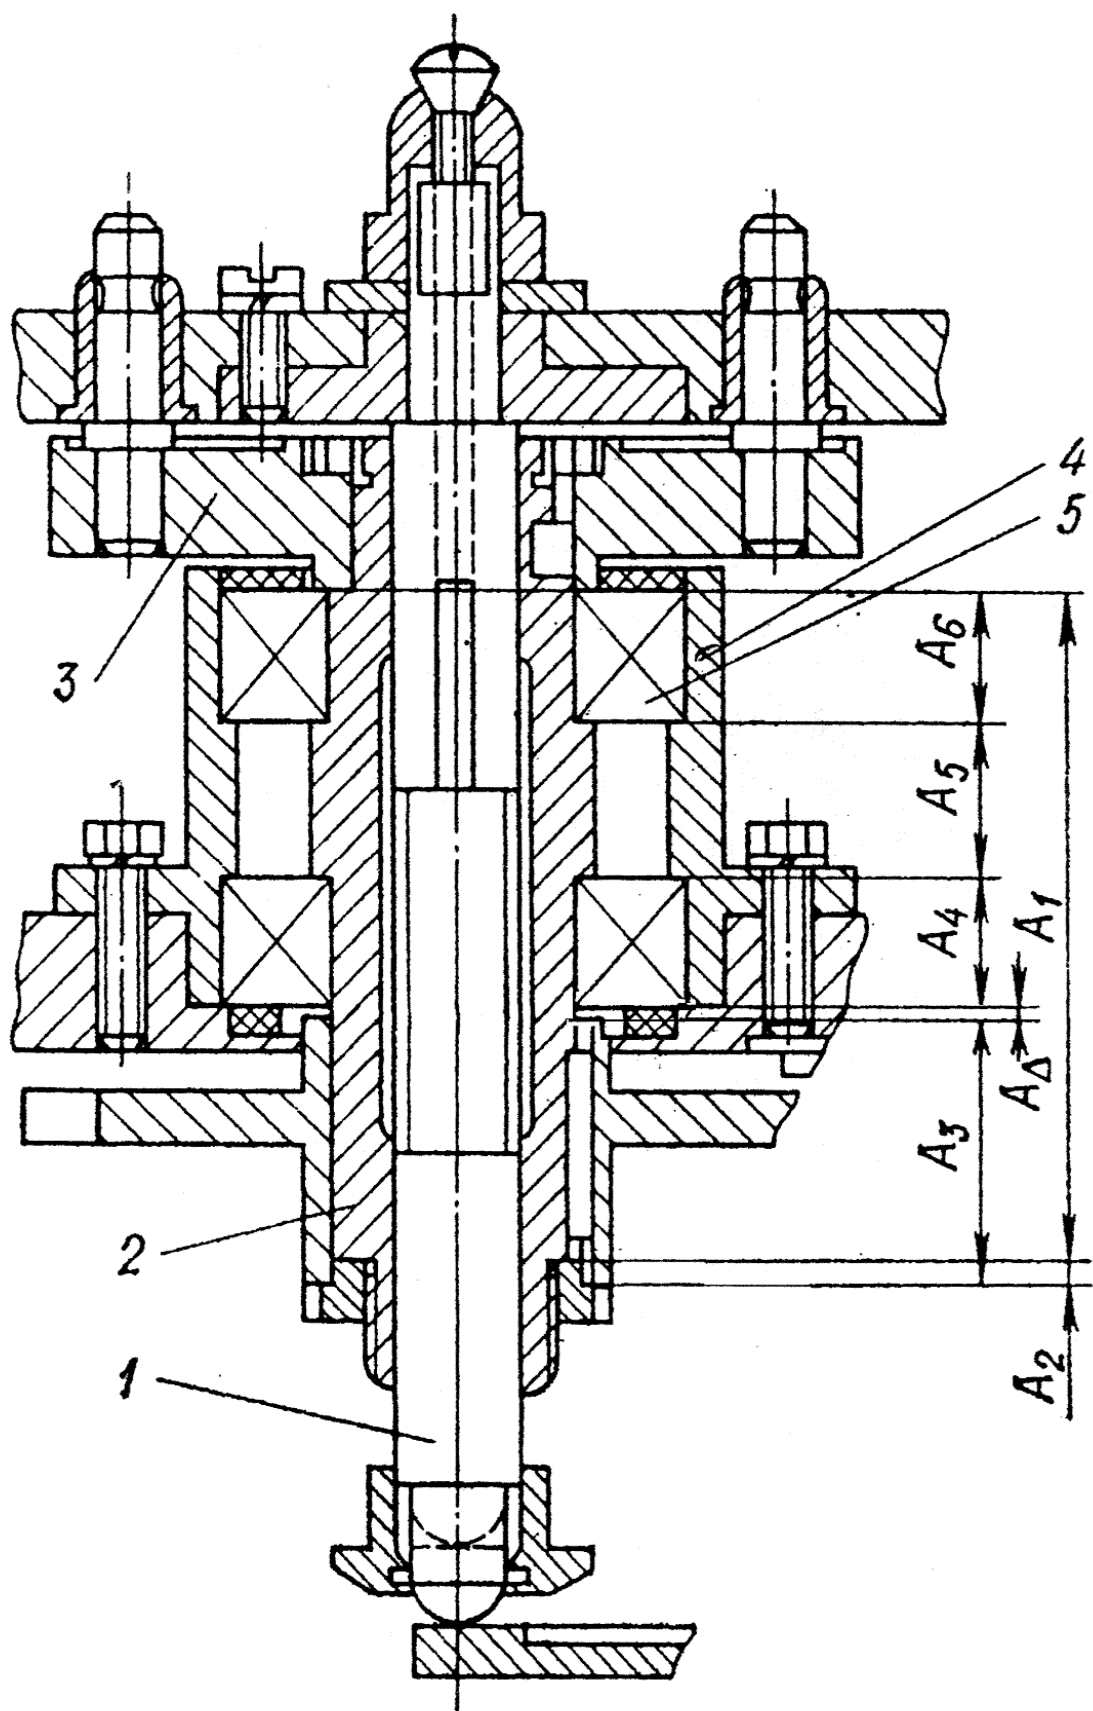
Узел подшипникового соединения: 1 – ось; 2 – вал; 3- диск;
